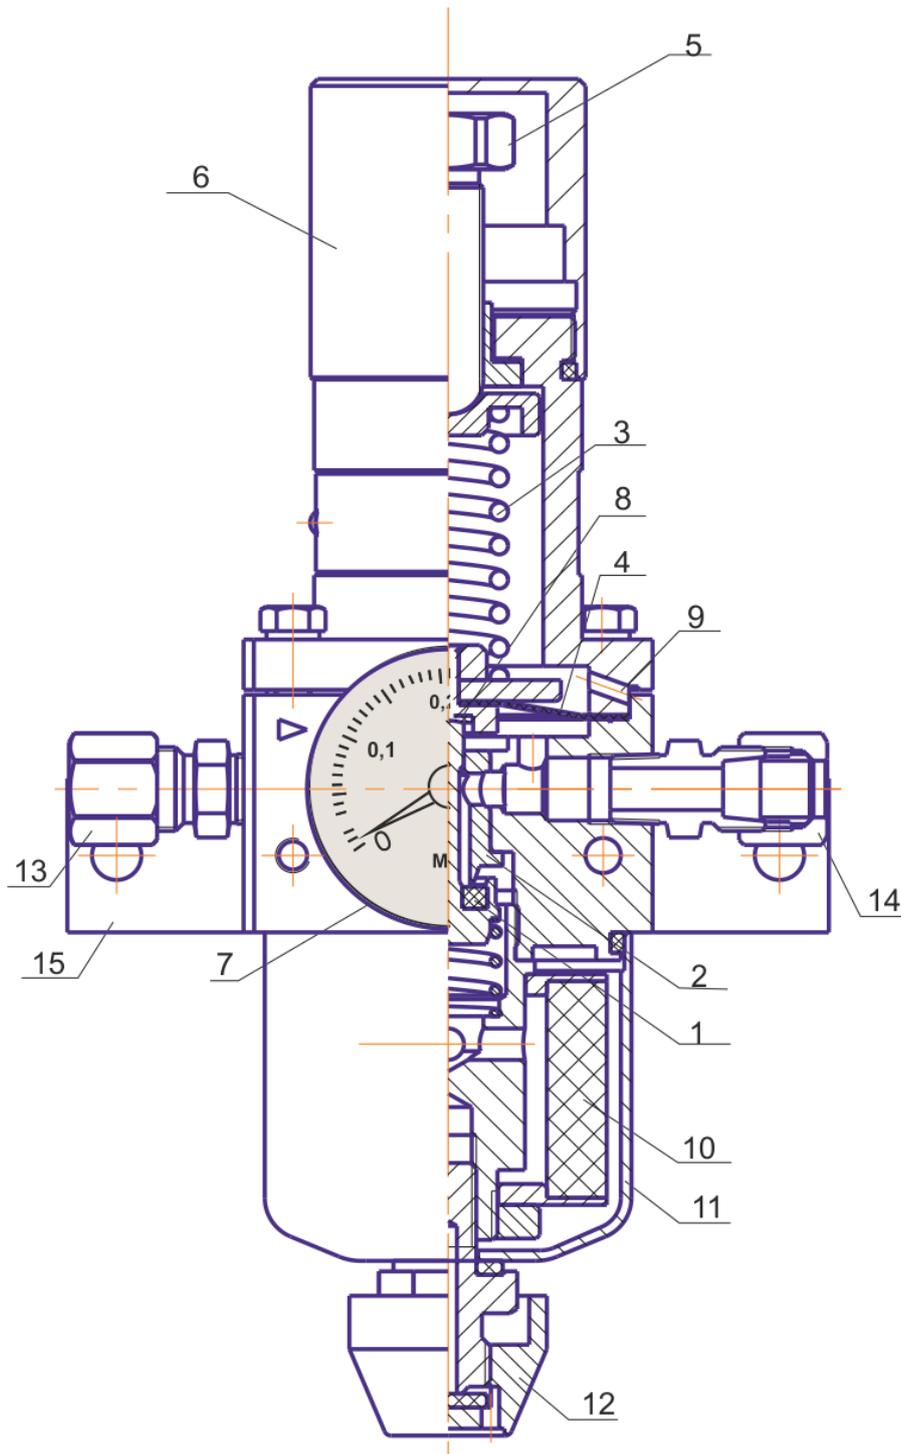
Конструкция редуктора РДФ-01М1
